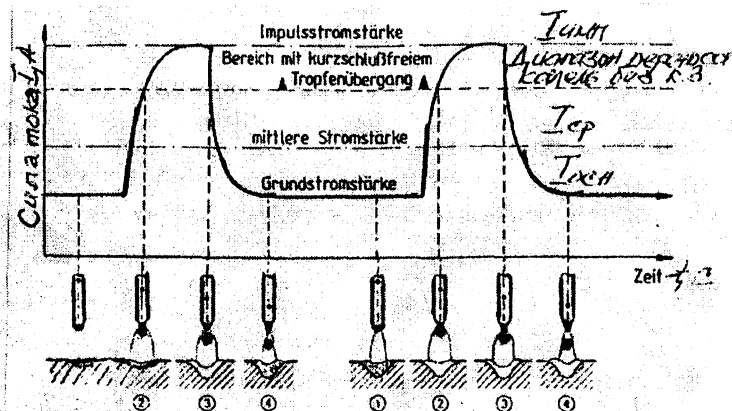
Переход электродного металла в сварочную ванну при ИДСПЭ 1 - нагрев торца электрода; 2 - образование капли на торце; 3 - сужение шейки и вытягивание капли в направлении сварочной ванны; 4 - отрыв капли и ее переход в сварочную ванну мелких капелек, образующихся из шейки при отрыве капли от электрода
